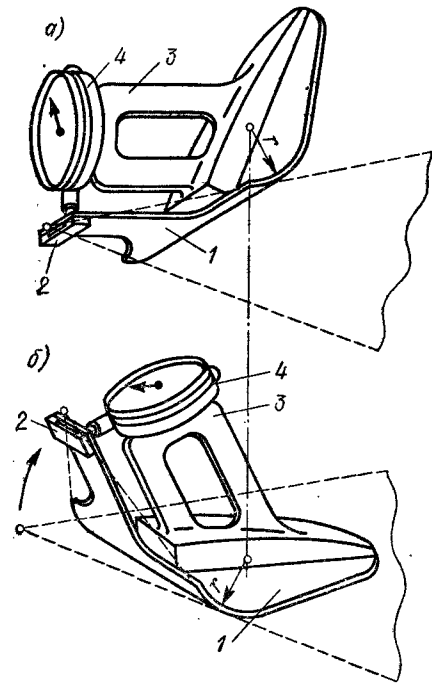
Прибор „Flex“ для испытания на загиб угла
